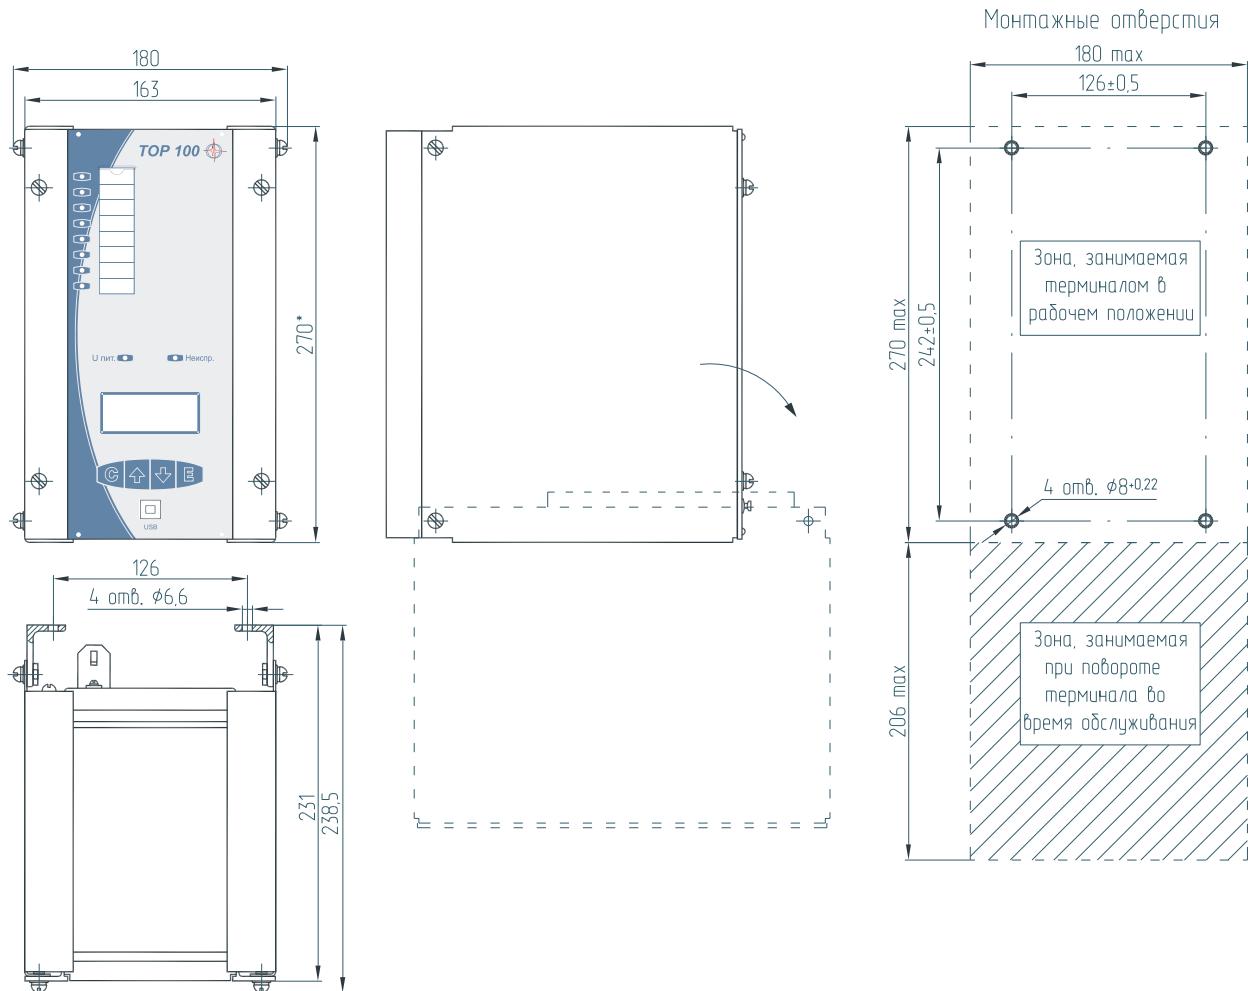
Габаритные и установочные размеры для навесного монтажа
